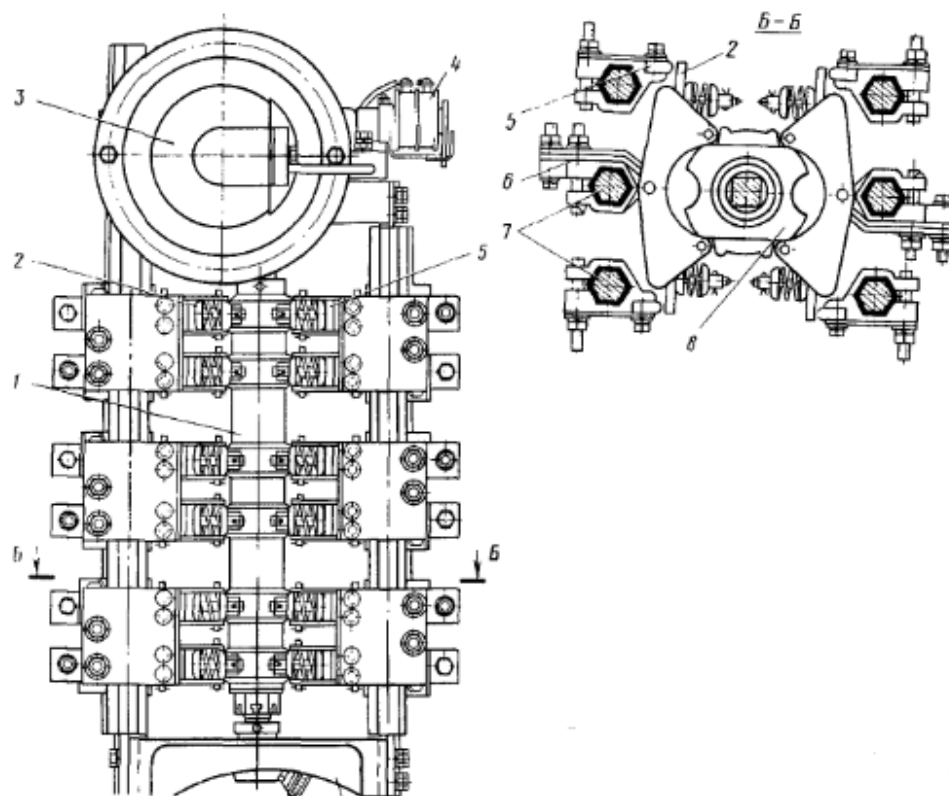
Переключатель электропневматический кулачковый типа ППК-8063 (реверсор)
